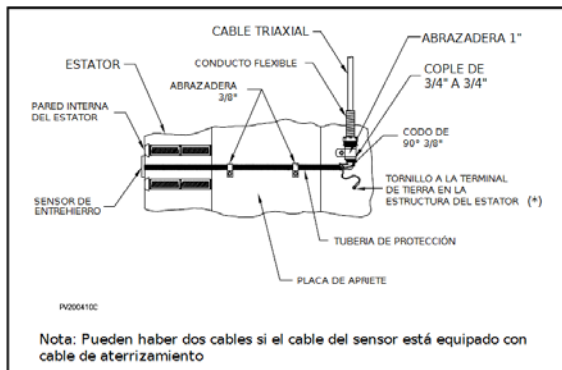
Ensamble de la parte superior de la carcasa del estator.
